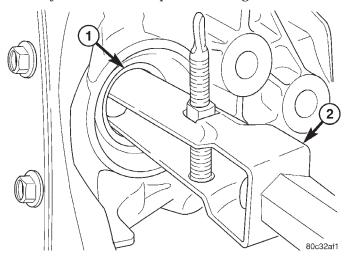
EXTRACTOR DE COJINETE DEL EJE
